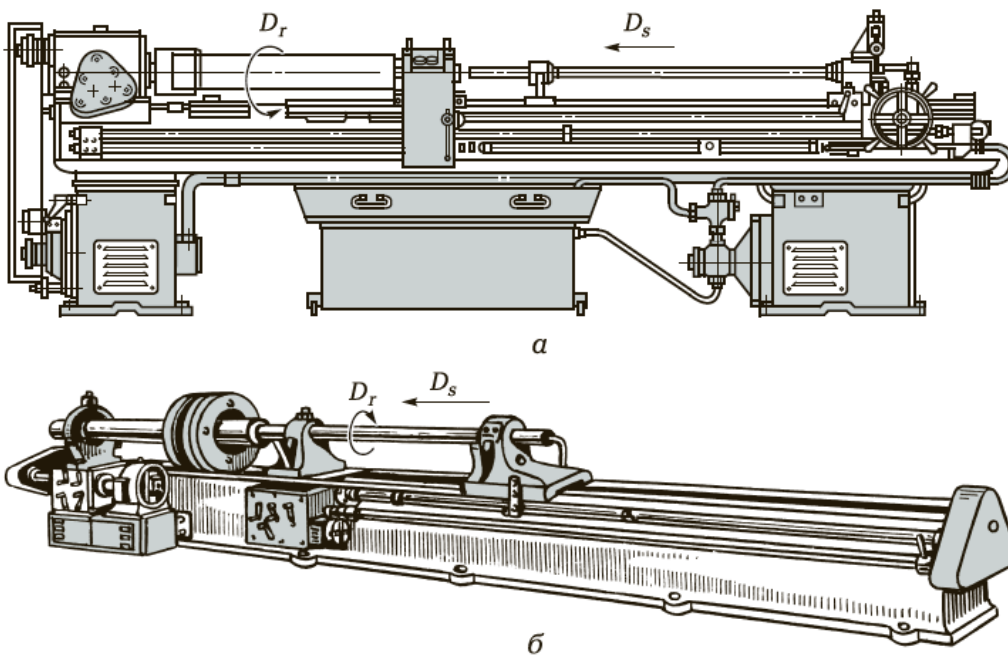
Горизонтально-сверлильные станки для глубокого сверления вращающихся заготовок (а) и (б):
